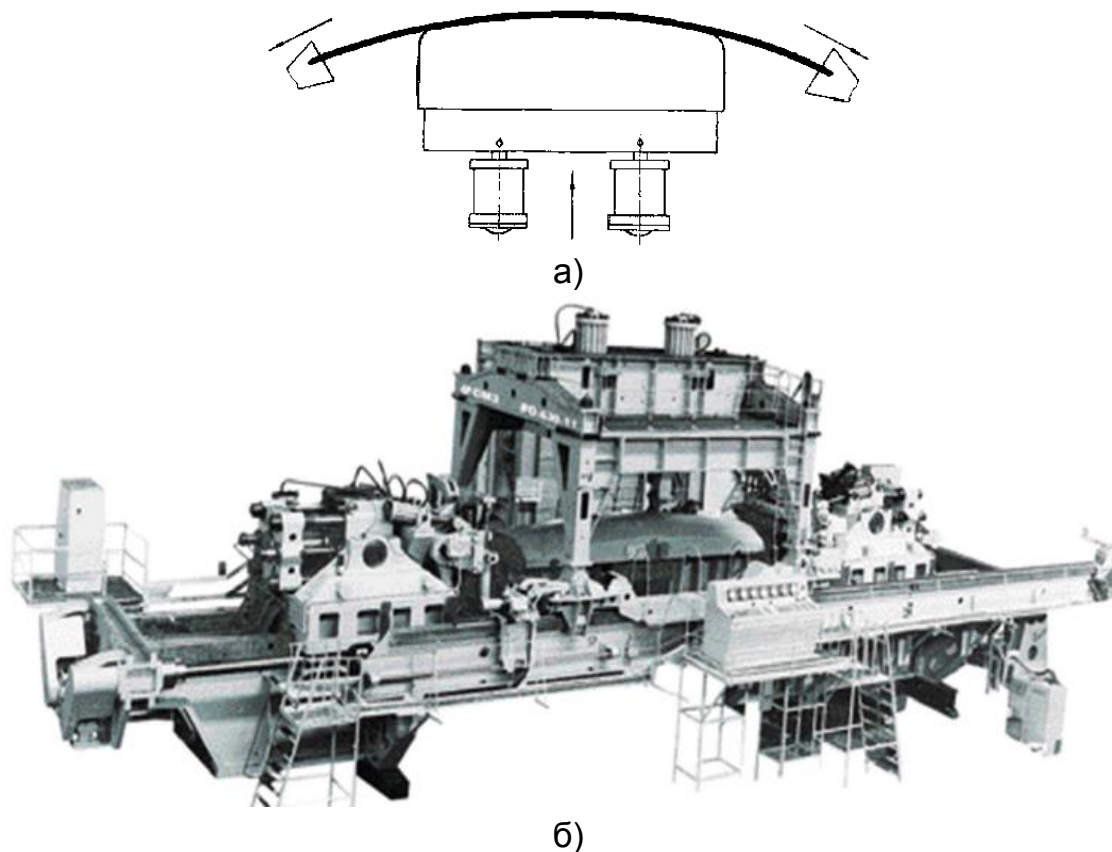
Формообразование заготовки растяжением с подъемом пуансона (а), пресс продольной обтяжки РО-630 (б)
